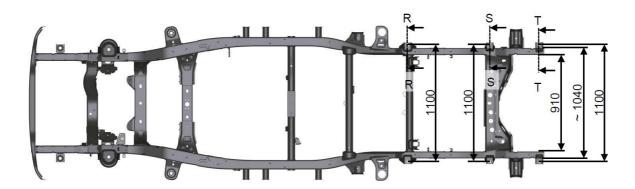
Vista dall'alto del telaio a scala dell'Amarok DC
